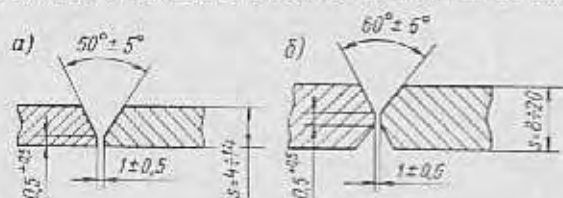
Конструктивные элементы подготовки кромок листового титана и титановых сплавов толщиной 3—20 мм под стыковую механизированную аргоно-дуговую сварку неплавящимся электродом (по ОН 26-01-71-68): а — V-образная разделка кромок; б — X-образная разделка кромок
